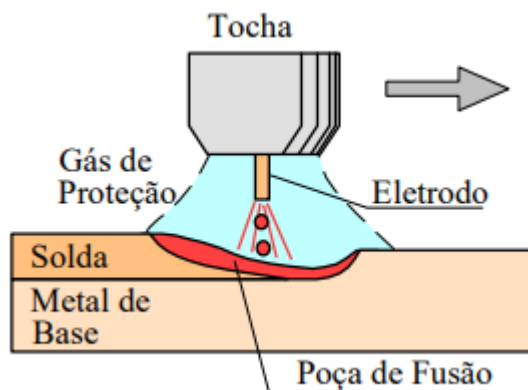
Esquema do processo de soldagem por MIG/MAG.
